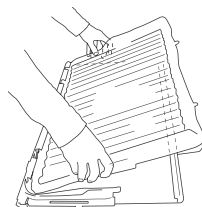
Retrait du couvercle des attaches arrière et des pièces de retenue latérales
